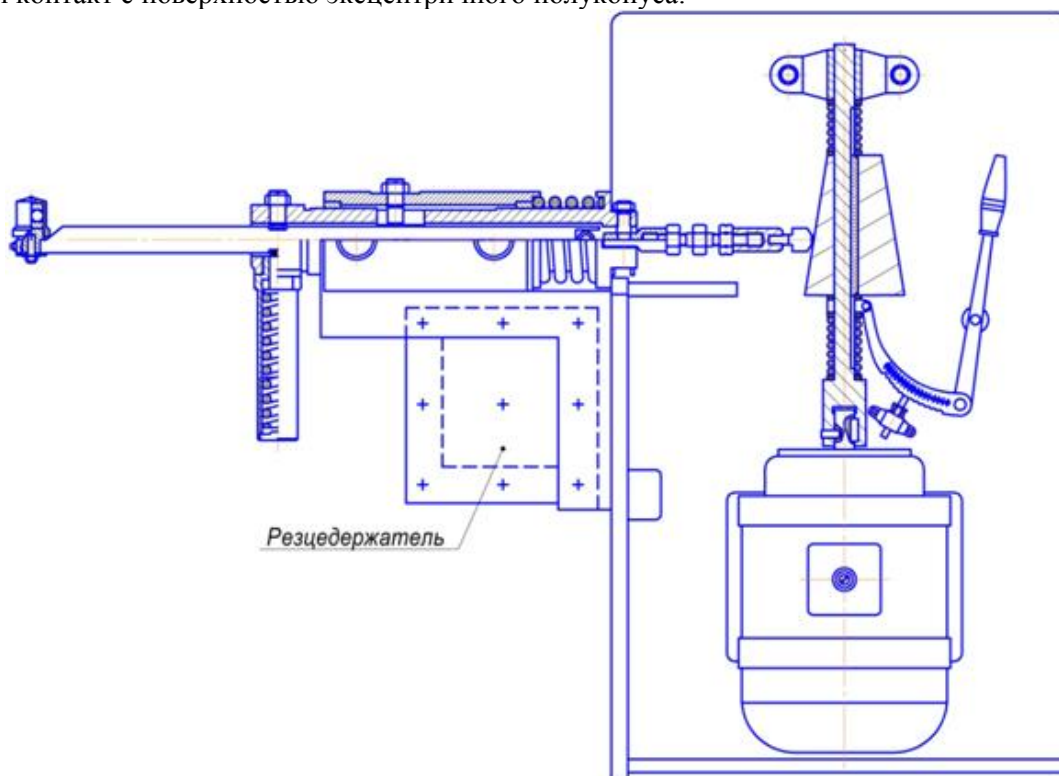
Схема приспособления с механизмом изменения амплитуды нанесения микрорельефа
